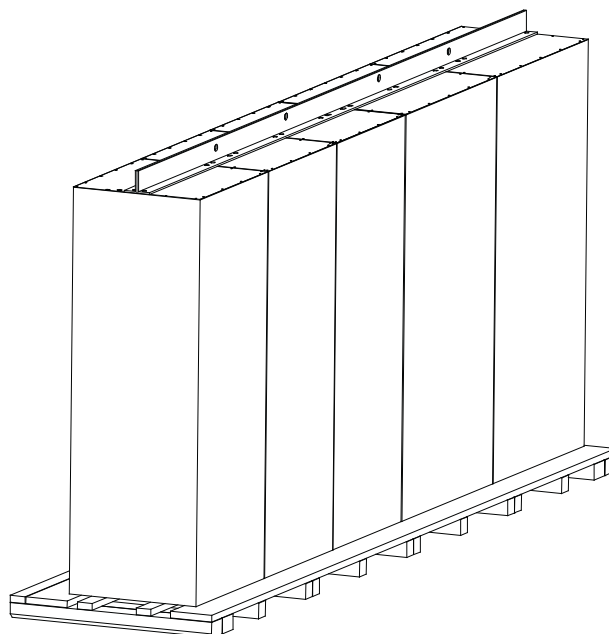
Преобразователь с нижними элементами для подъёма с помощью подвесных приспособлений
